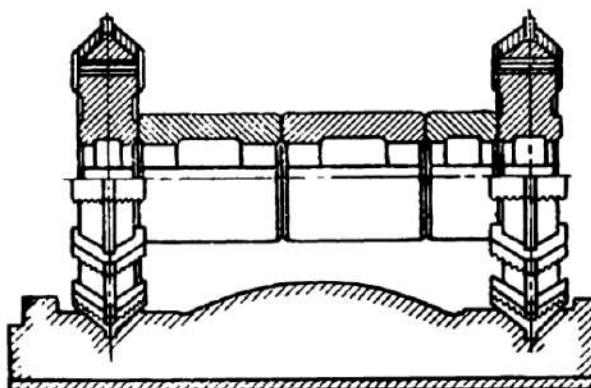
Наборы фрез для обработки двух торцевых деталей.
